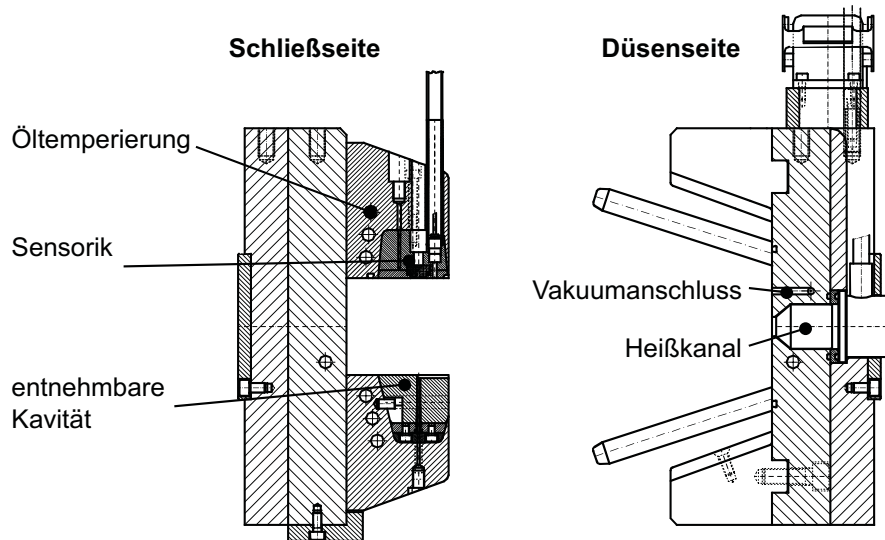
Aufbau des Versuchswerkzeugs
